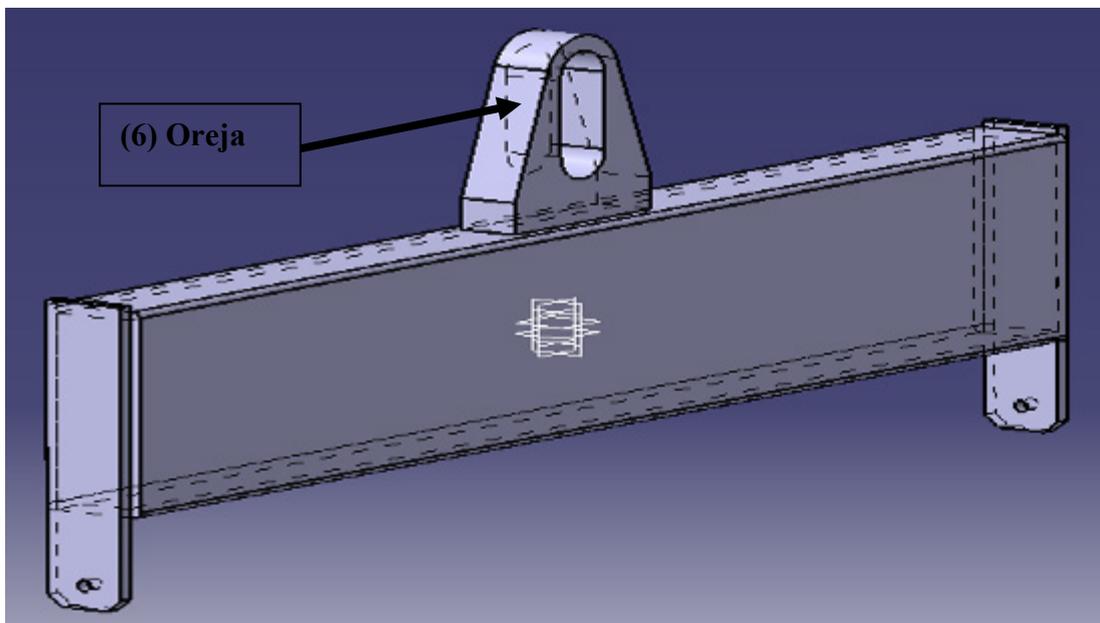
Oreja de carga montada junto con la placa de carga y la viga soporte.
